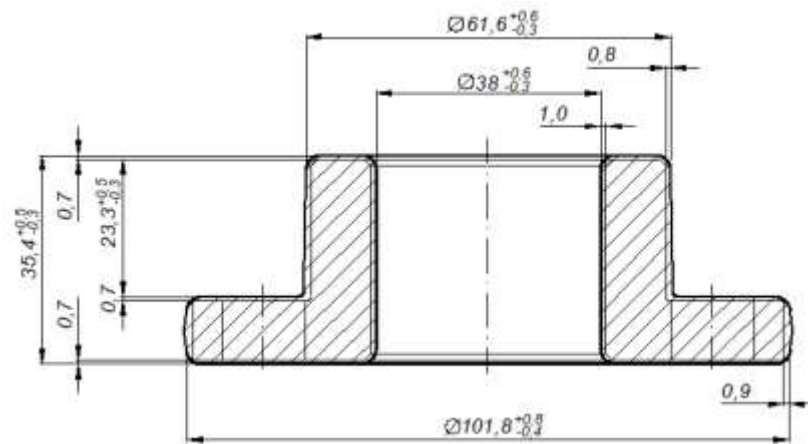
Ескіз закритої штамповки для гарячештампувального пресу
